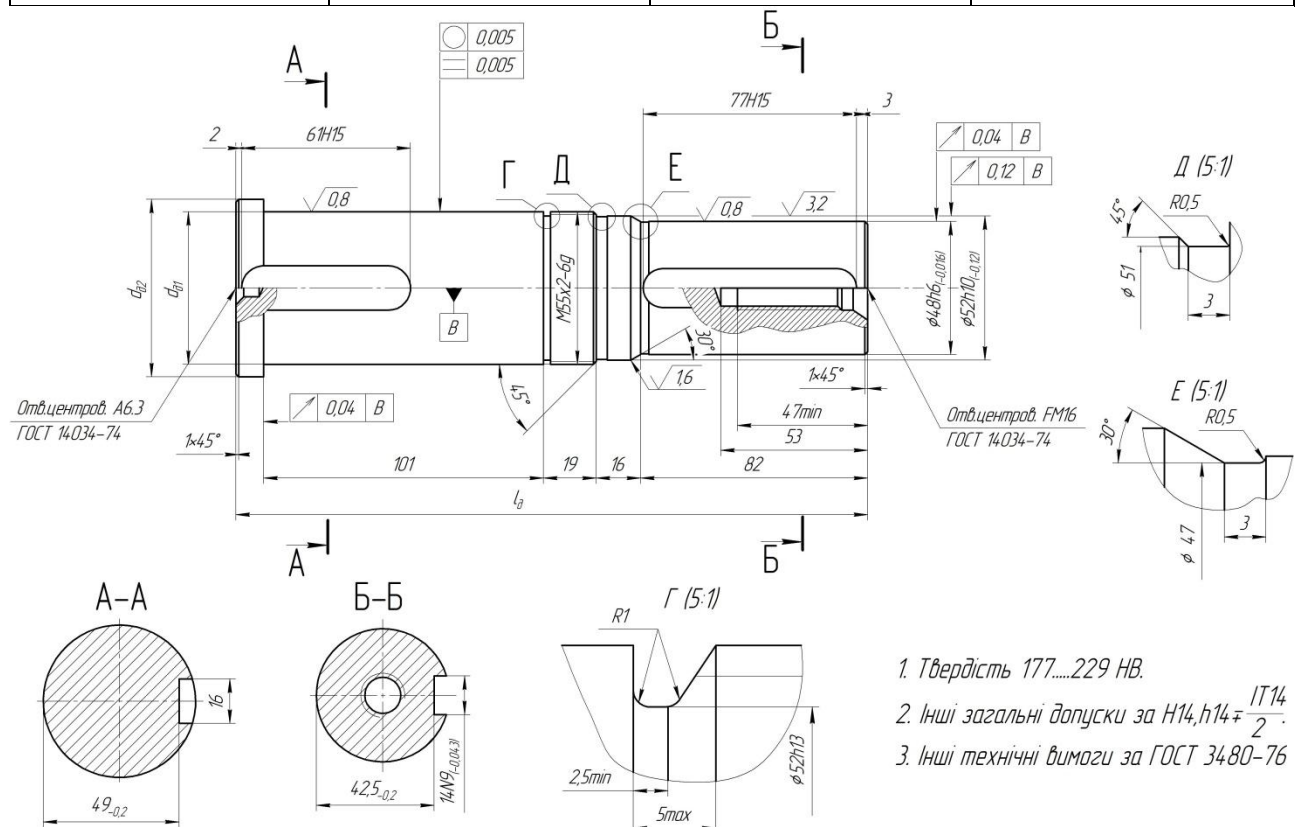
Робоче креслення заготовки деталі «Вал»
